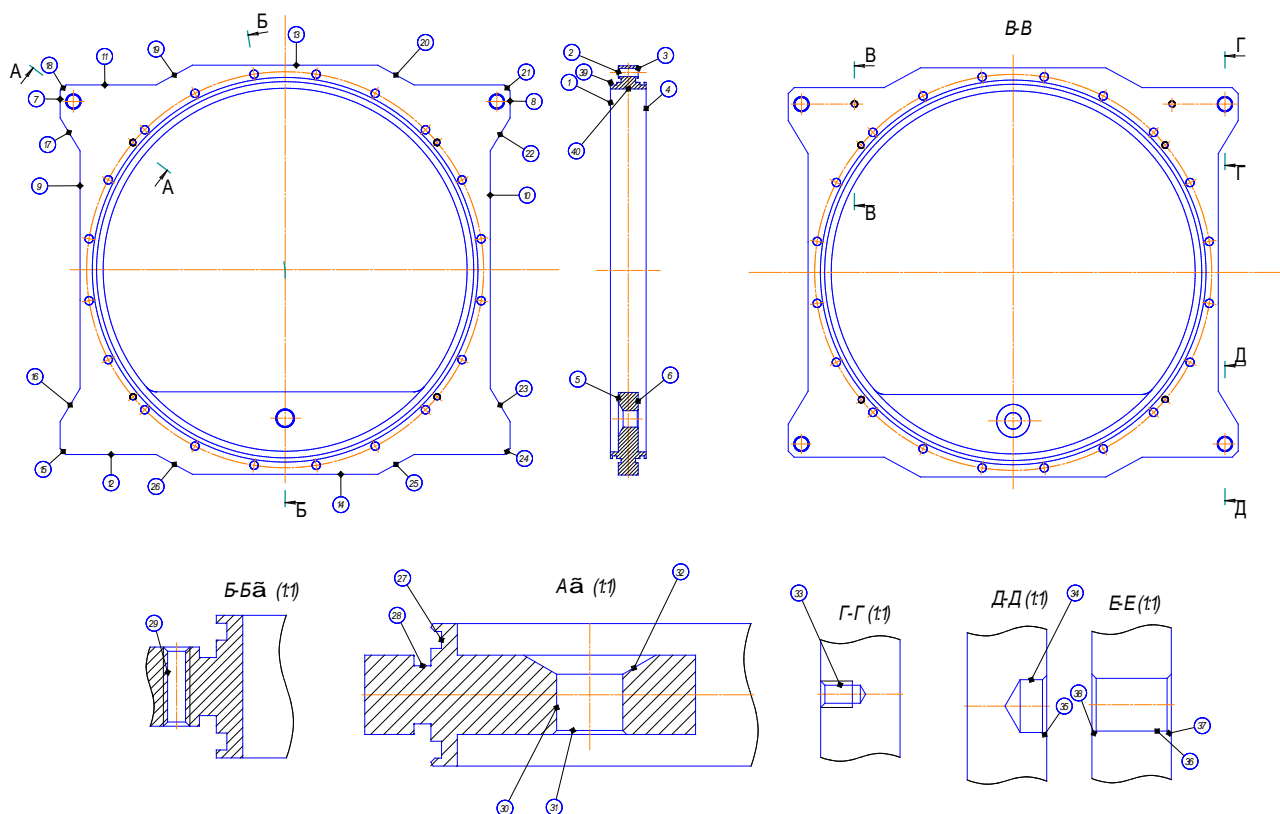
Эскиз детали с номерами обрабатываемых поверхностей
